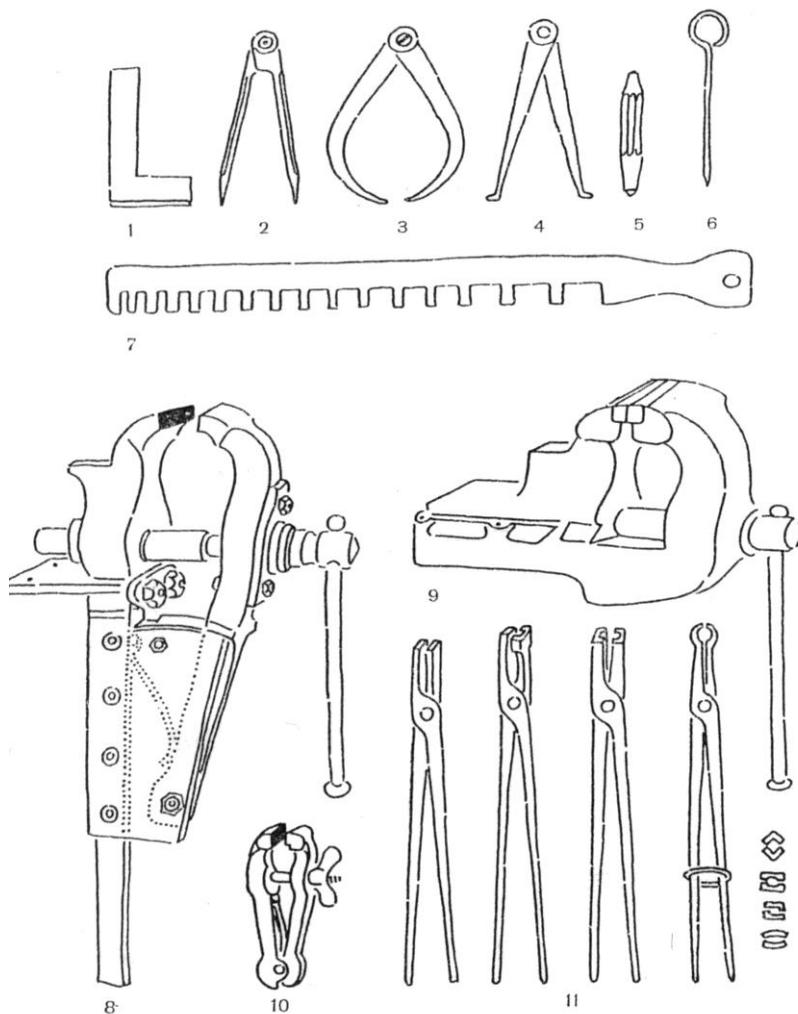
Вспомогательный инструмент для ручной свободнойковки:
